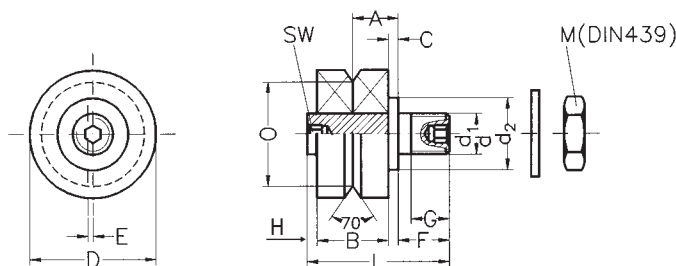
70° RK-Rolle mit kurzem Bolzen | Fig.1: 70° RK-roller with short bolt
